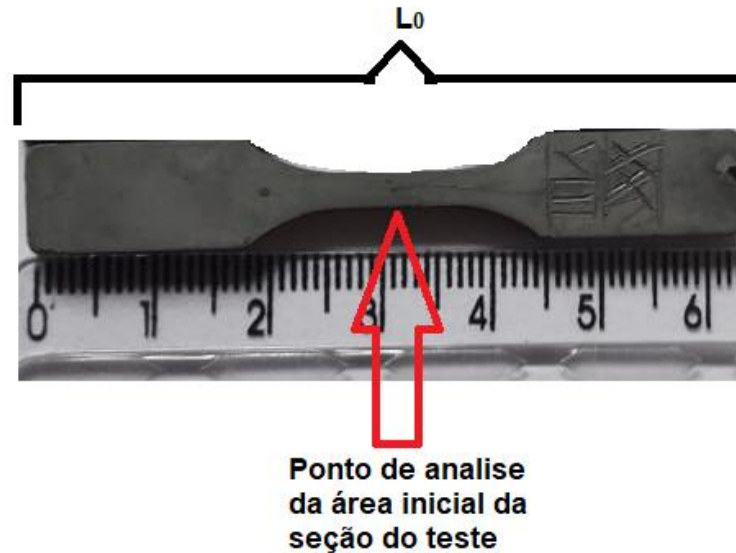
Moldagem de *dog bones* com carga injetável produzida.
